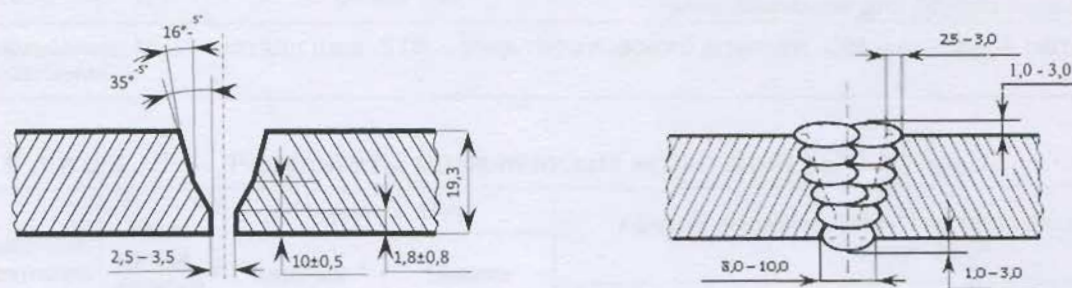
Геометрические параметры сборки контрольного сварного соединения и эскиз сварного шва КСС № 2
